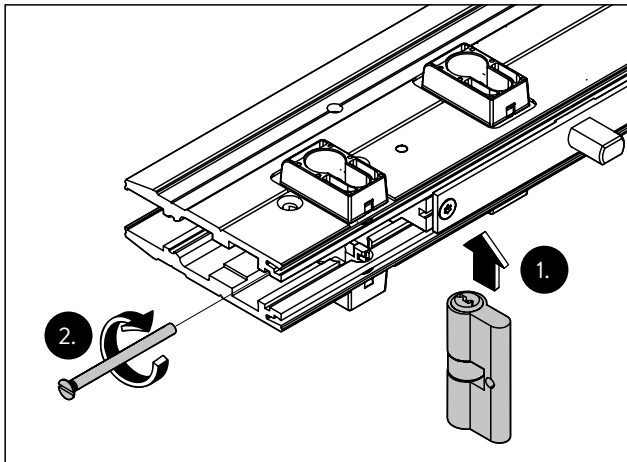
Den Schließzylinder einsetzen und verschrauben
